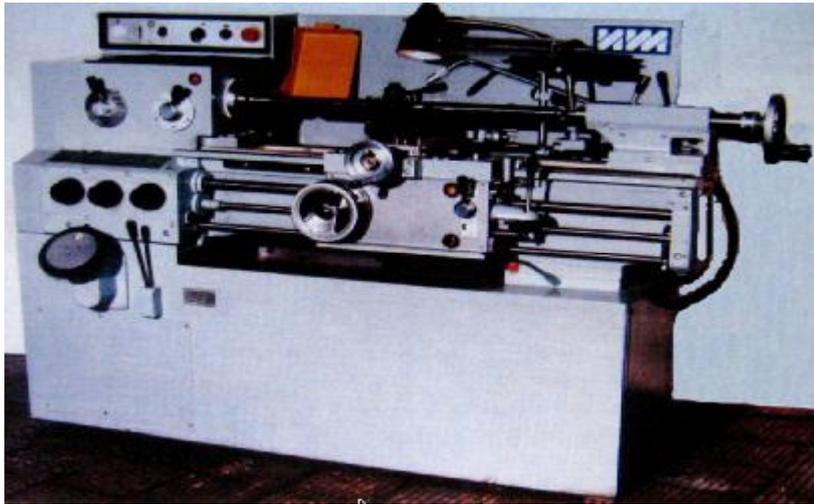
Универсальный токарно-винторезный станок 250ИТВМ01
